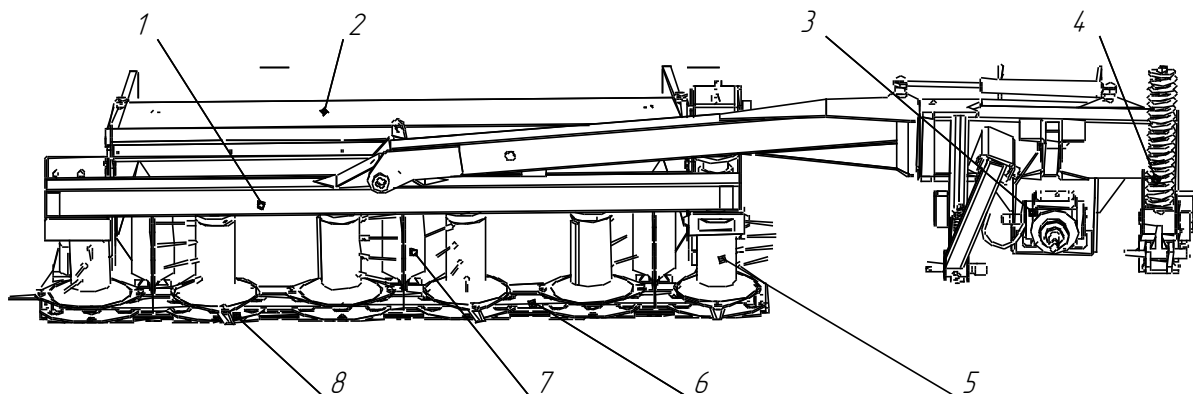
Пропонована конструкція модернізованої косарки: 1 – рама; 2 – кожух; 3 – редуктор; 4 – система навішування; 5 – ротор; 6 – брус; 7 – дека; 8 – башмак.
